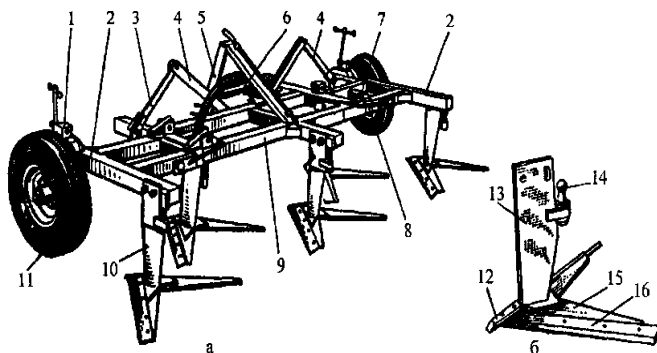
Культиватор-плоскорізь широкозахватний КПШ-5:
